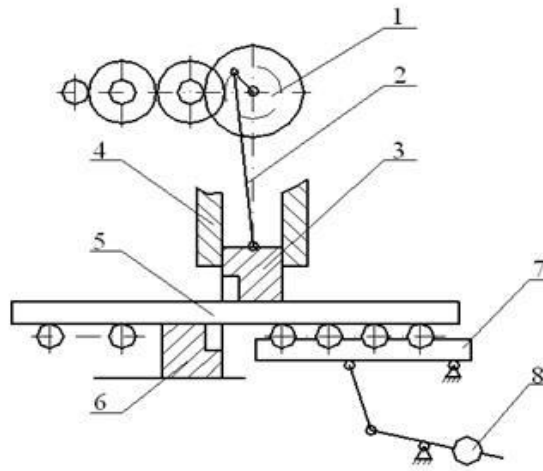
Кінематична схема ножиць з верхнім різом
